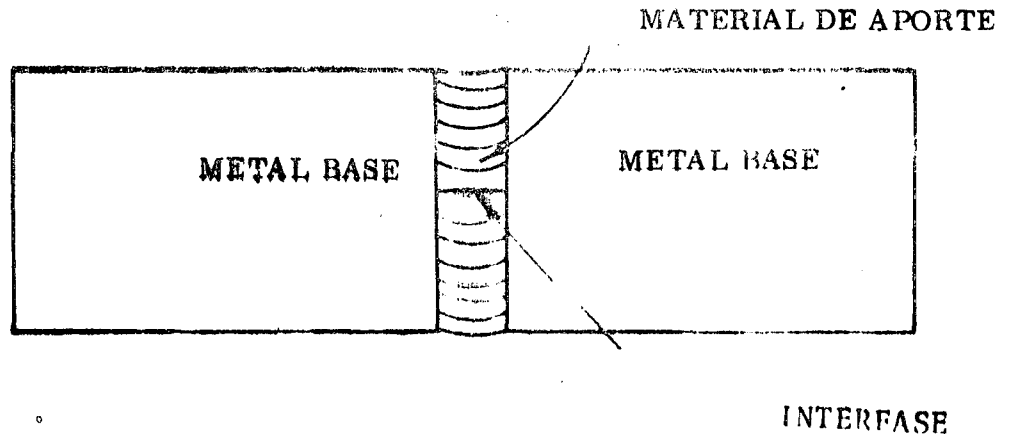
Falta de fusión entre dos partes del mismo cordón de soldadura.
